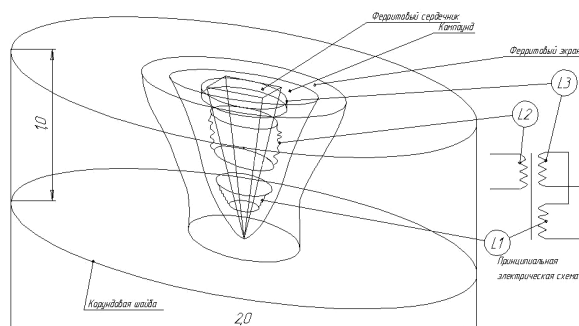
Схема конструкции СМВТП для прямых измерений
